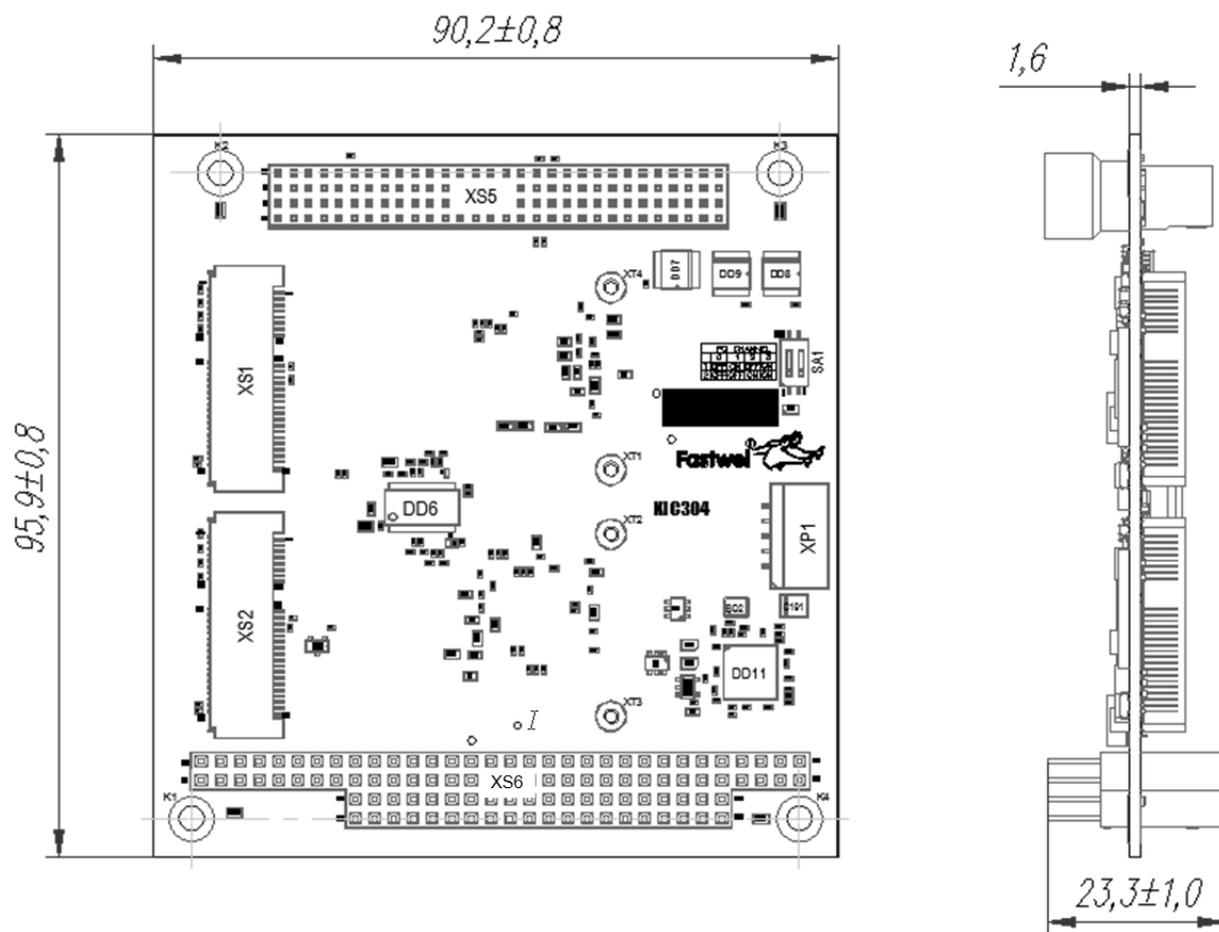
3 - Расположение основных компонентов и габаритные размеры (вид сверху, вид сбоку)
